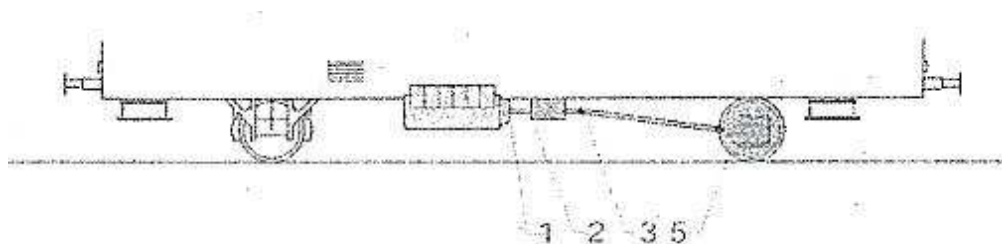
Základní uspořádání mechanického přenosu výkonu [5]
